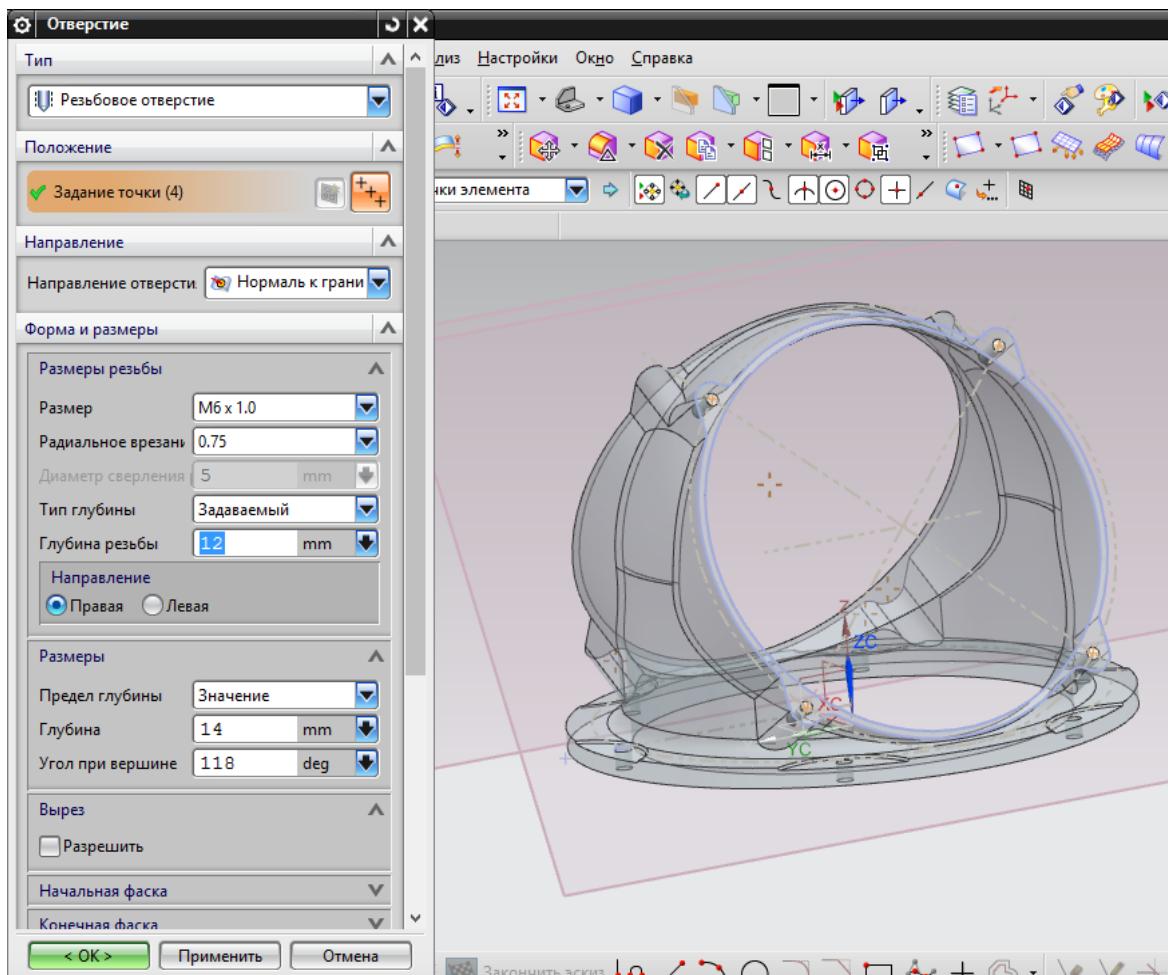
Создание резьбовых отверстий на фланцевой части корпуса
